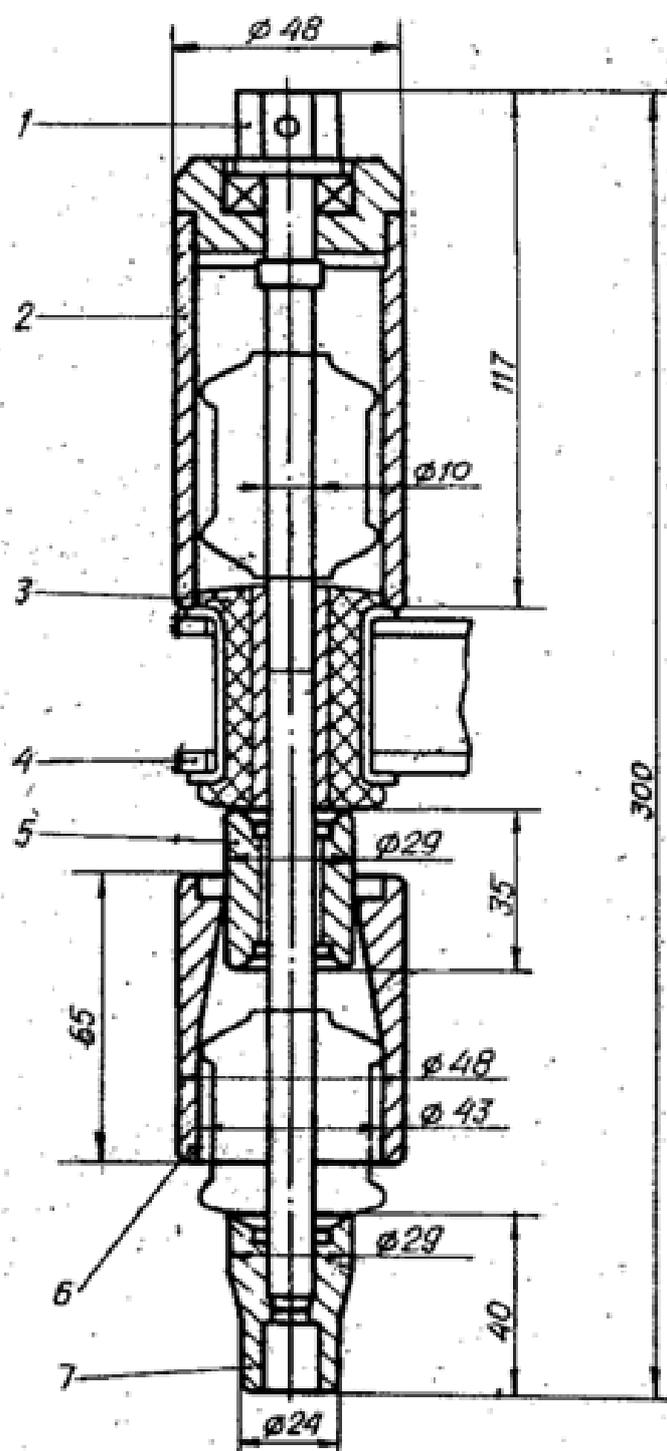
Запрессовка и выпрессовка сайлентблока рычага передней подвески: 1 - винт; 2 - стакан; 3 - сайлентблок; 4 - рычаг; 5 - втулка для выпрессовки; 6 - втулка направляющая; 7 - толкатель для запрессовки.
